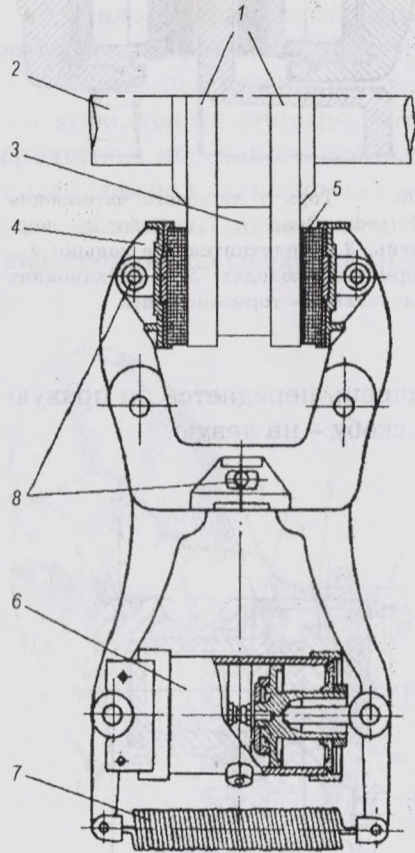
Клещевой тормоз: 1 – тормозной диск; 2 – ось колесной пары; 3 – ребро жесткости; 4 – башмак; 5 – фрикционный элемент; 6 – пневмоцилиндр с двумя поршнями; 7 – пружина растяжения; 8 – шарнирное крепление
